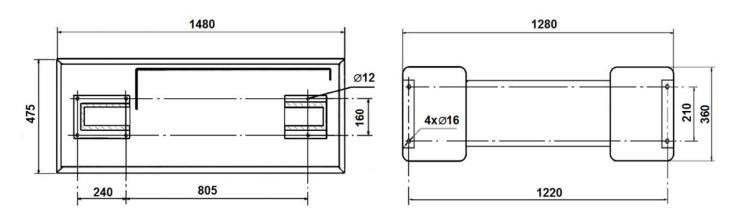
Schema der Ankerschraubenbohrungen des Drehmaschinenbattes (links) und des Ständers (rechts)
